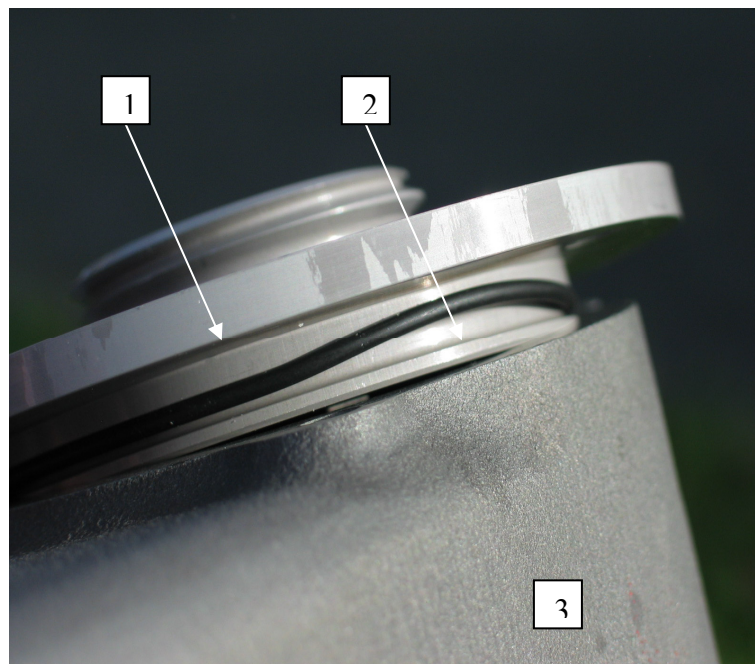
Пример установки в картер двигателя крышки фильтра с неправильным положением уплотнительного кольца.
